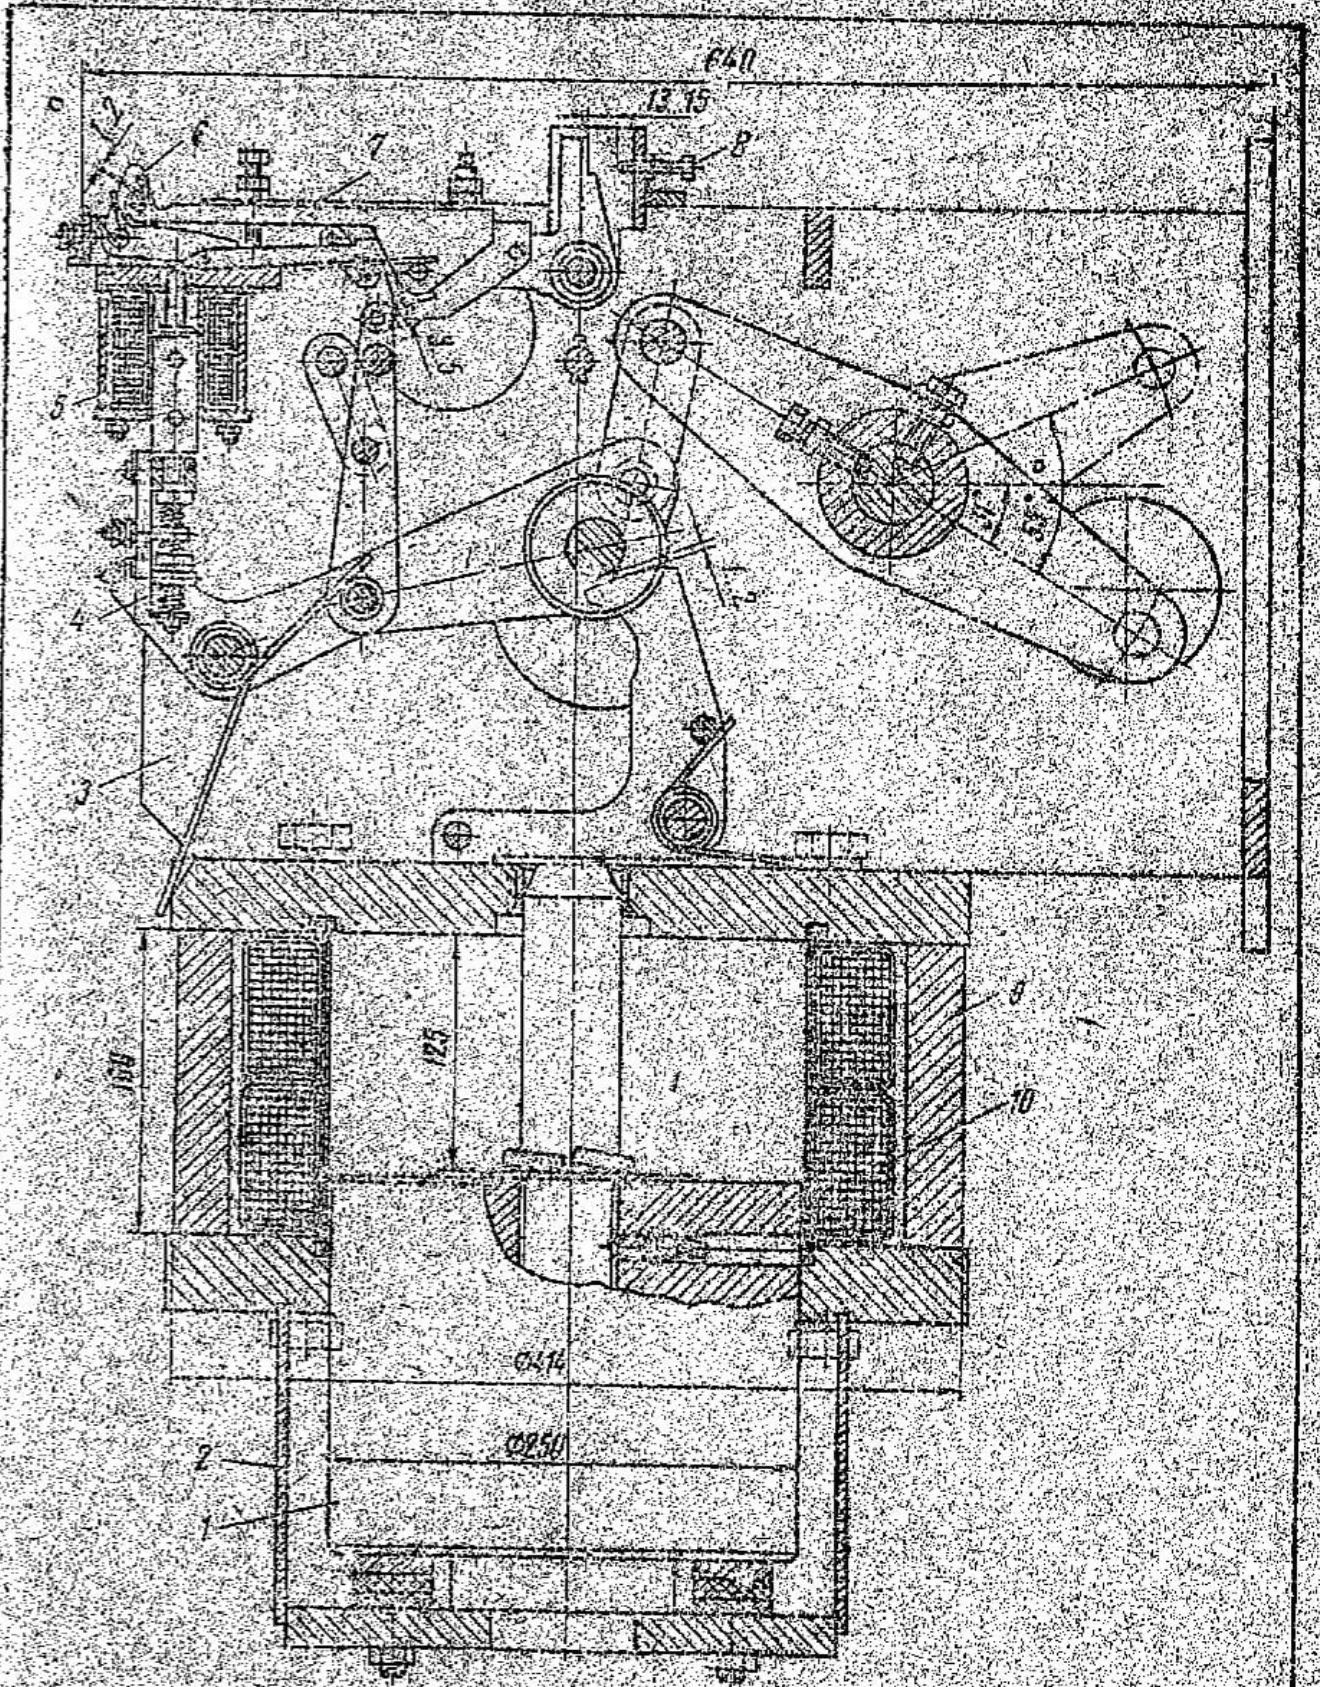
Быстро действующий электромагнитный привод типа ПЭ-33:
